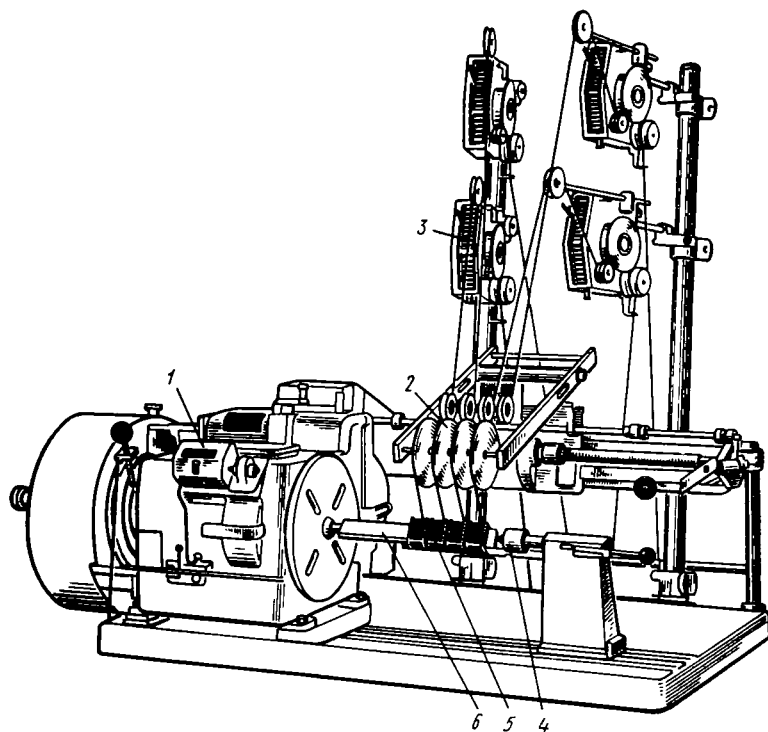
Полуавтоматический станок для намотки обмотки на каркас
